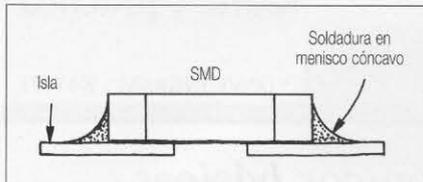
Vista lateral de la soldadura de un SMD.
